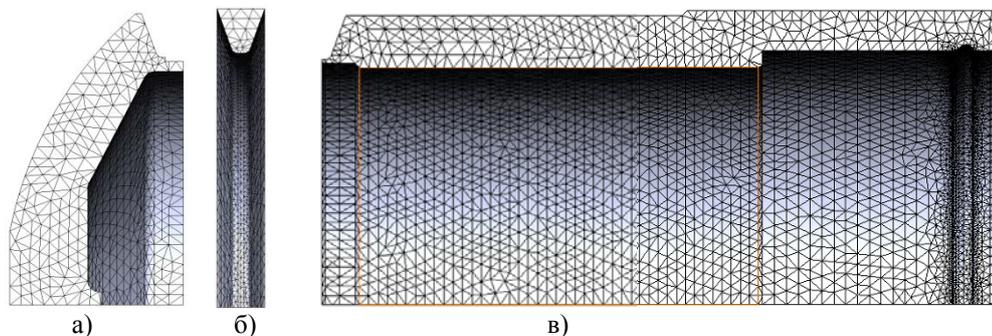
Построение сетки для модели цилиндра гидростойки в автоматическом режиме (а – дно цилиндра; б – сварной шов, в – рабочий цилиндр)
